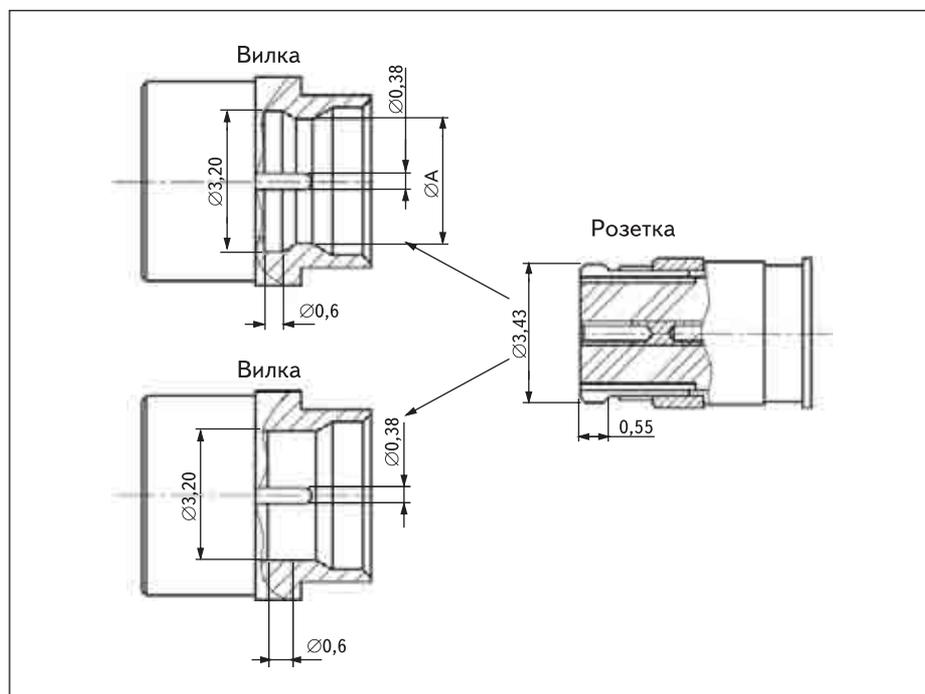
Конструкция snap-on соединителей SMP: а) блокировка, б) скользящее соединение
